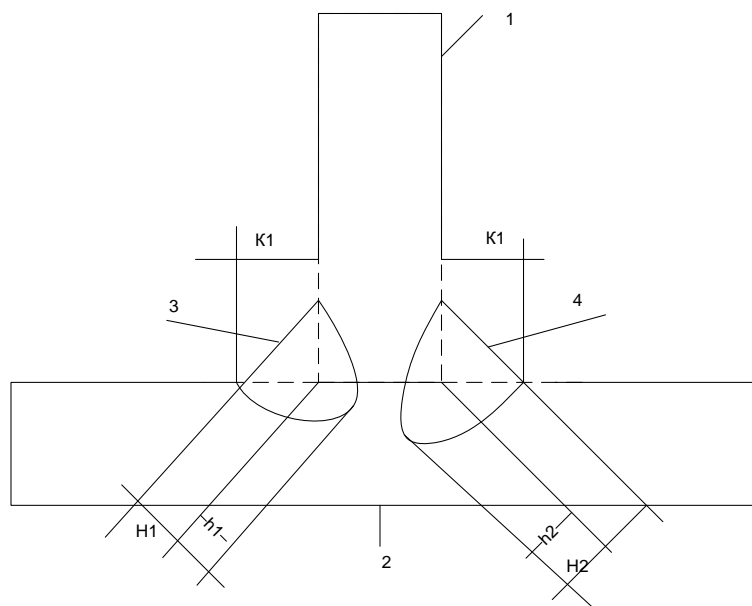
Форма сварных швов при сварке по известному способу
